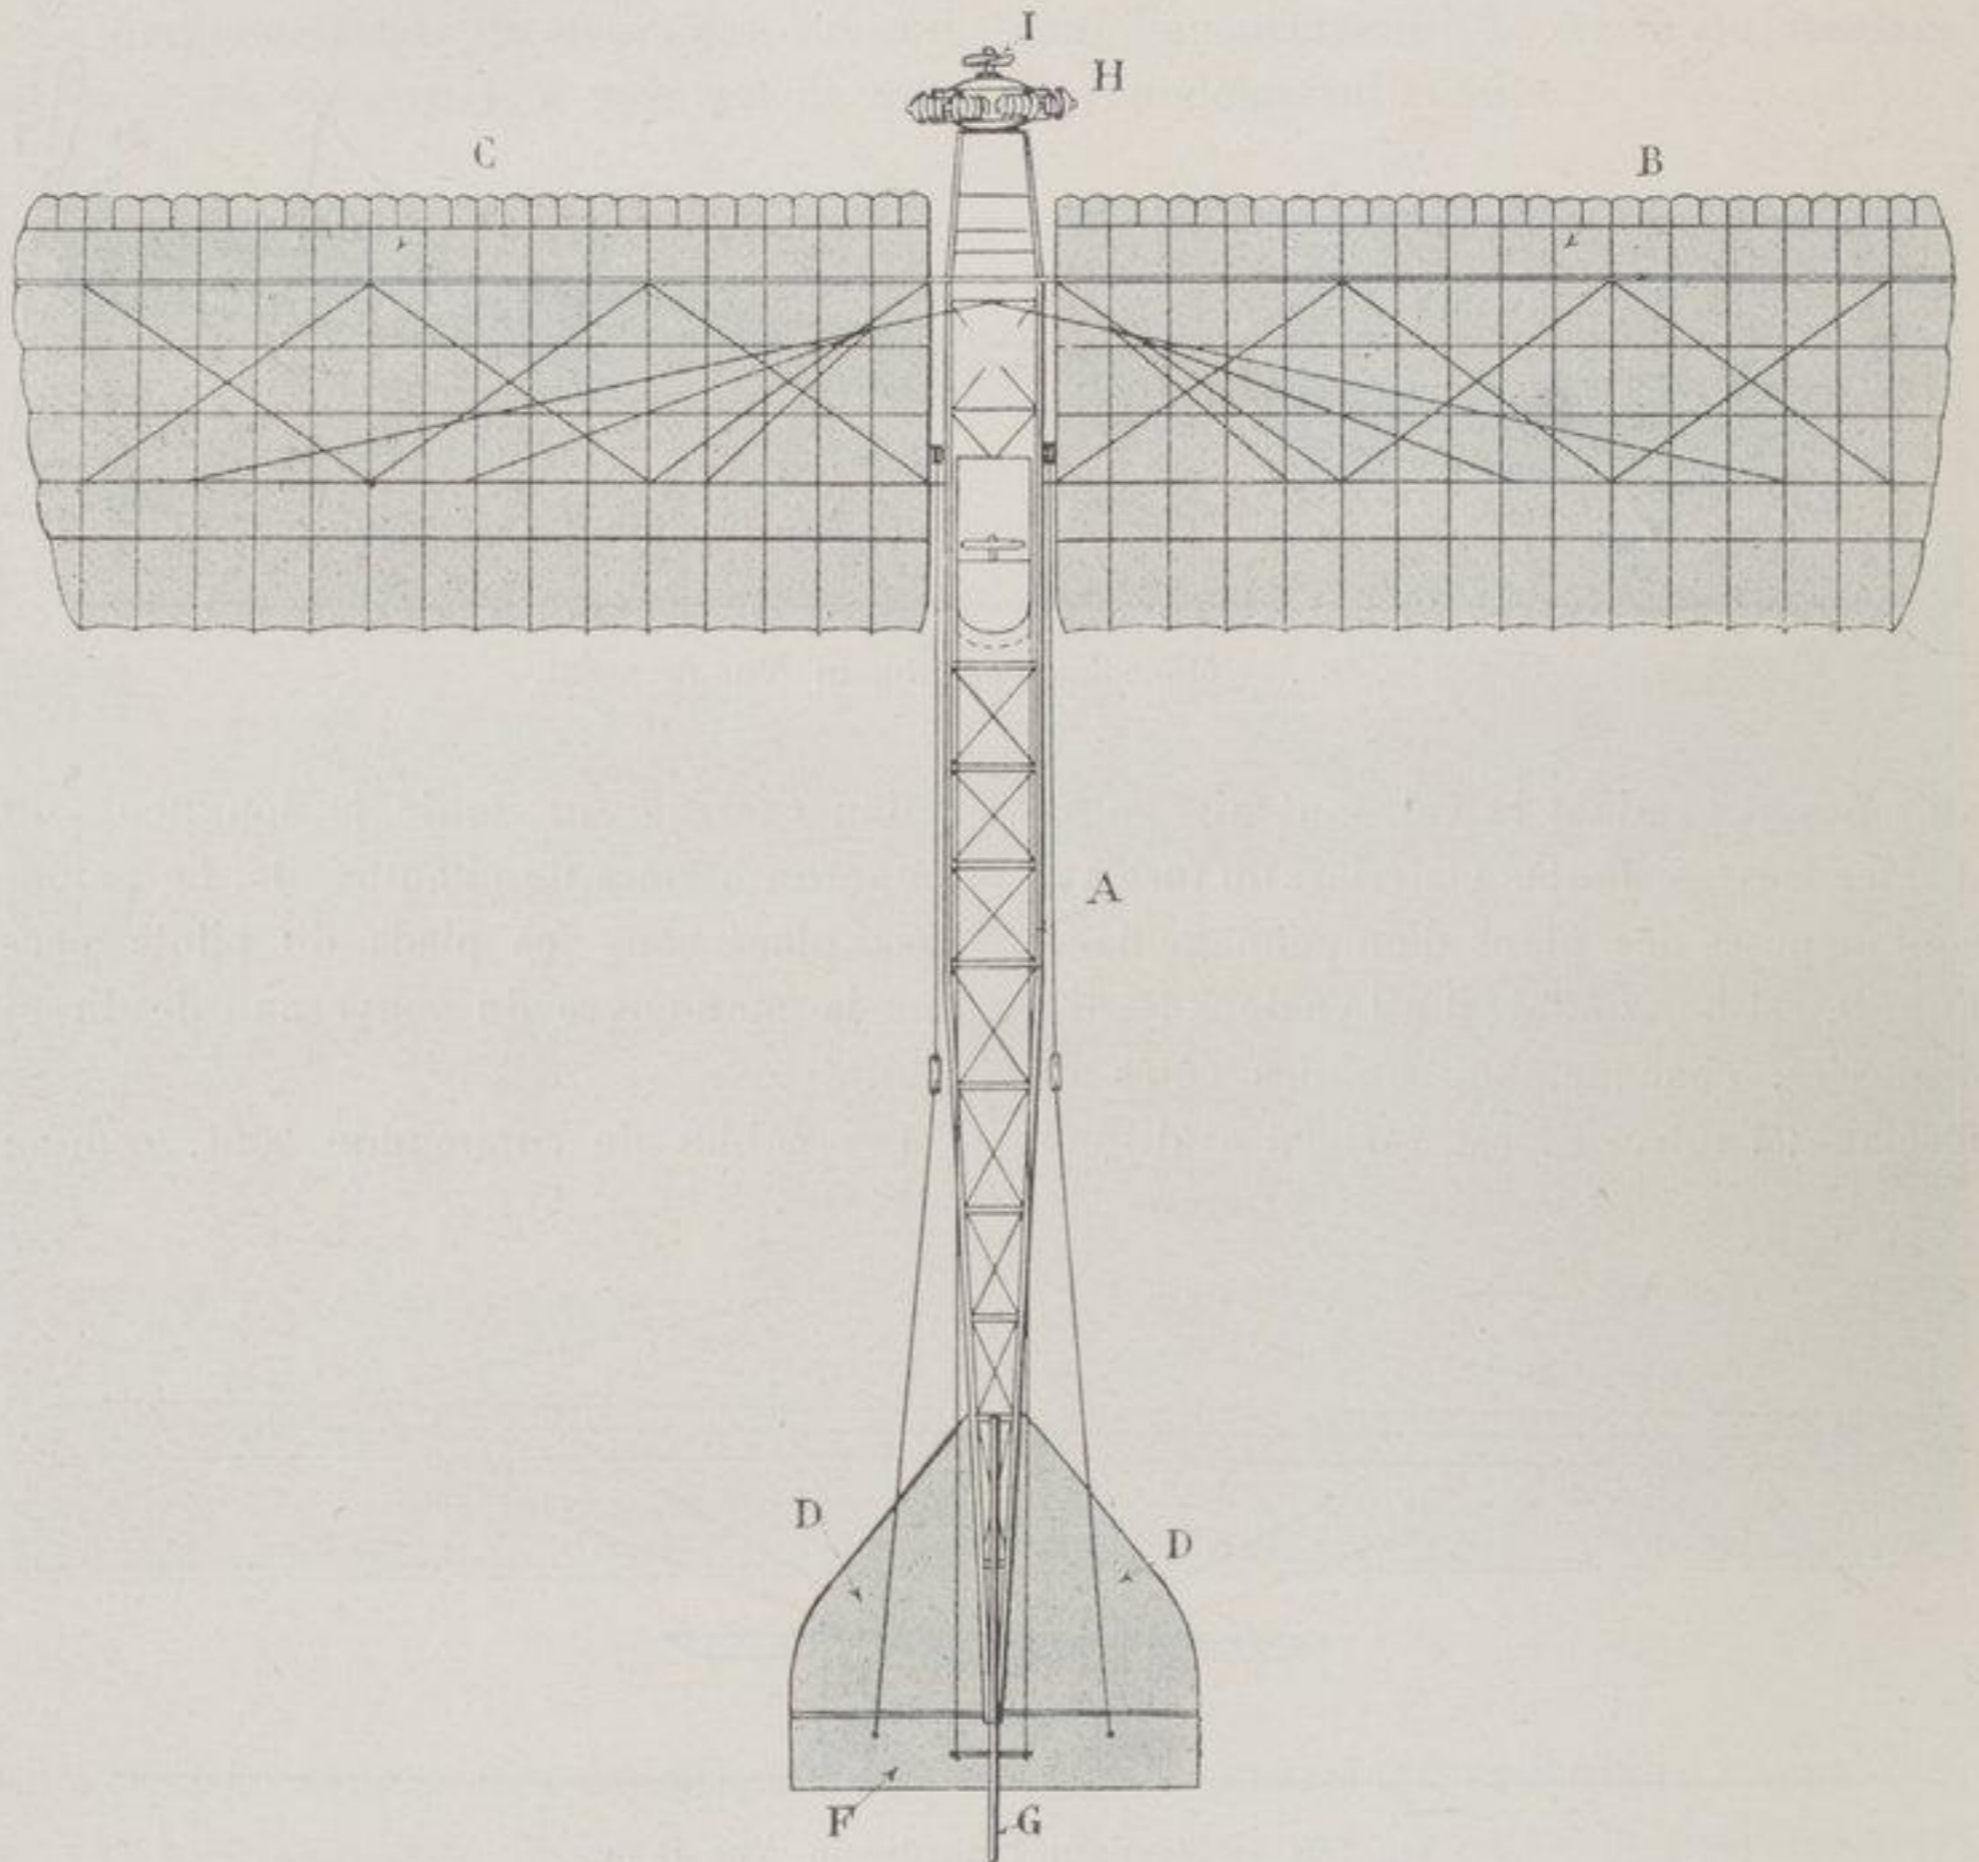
Monoplan Deperdussin. Vue en plan.
